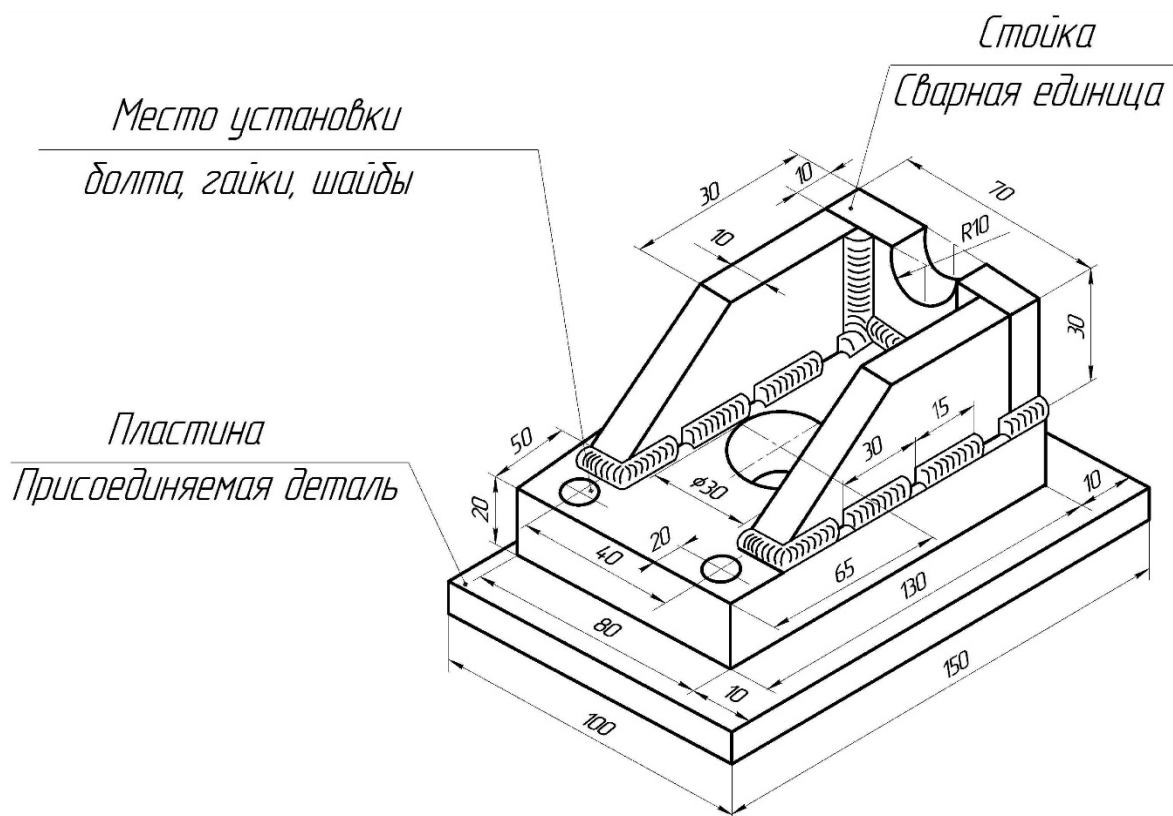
Наглядное изображение сварной единицы «Стойка» с пластиной
